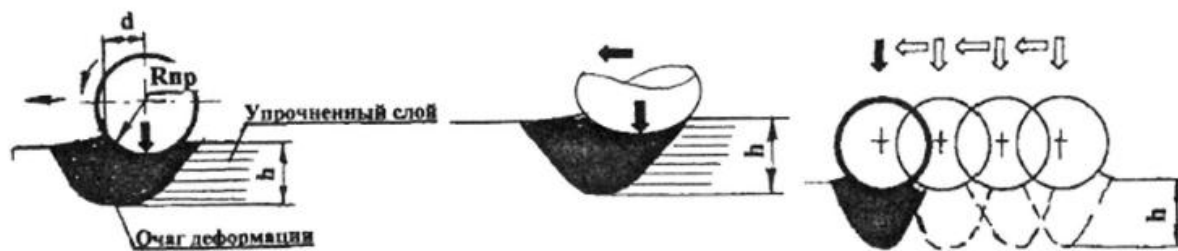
Основні схеми взаємодії деформуючого елемента з оброблюваної поверхнею: а - кочення; б - ковзання; в - впровадження
